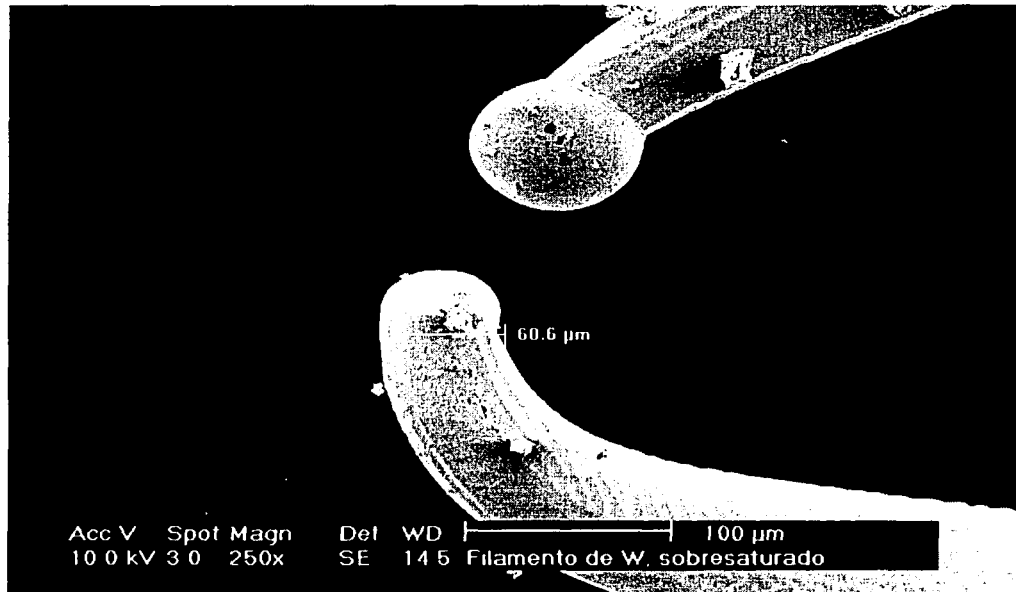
Vista completa de un filamento de tungsteno (falla por sobreesaturación).
